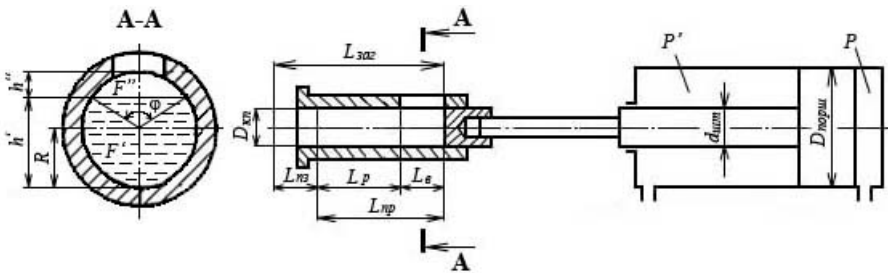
Розрахункова схема механізму пресування машини лиття під тиском
